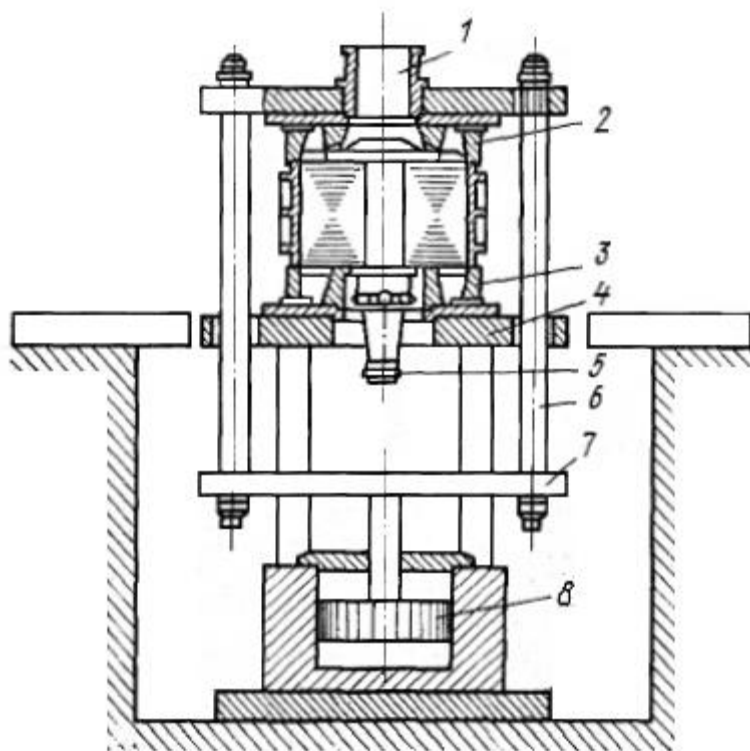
Установки для заливки роторов статическим способом: 1-литниковая чаша; 2-верхняя часть кокиля; 3-нижняя часть кокиля; 4-основание; 5-нижняя часть оправки; 6-механизм движения тяг; 7-форма; 8-поршень
